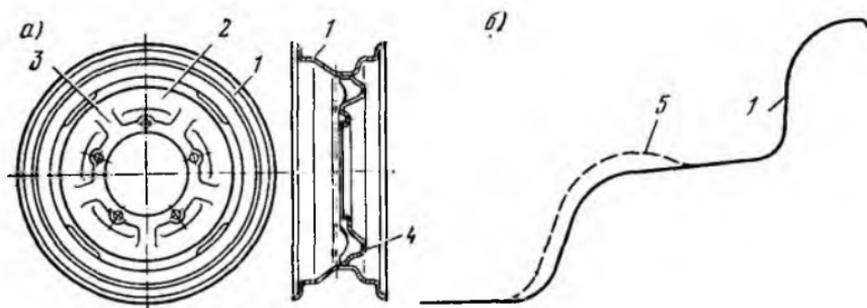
Колесо легкового автомобиля (а) и профиль полки обода (б) для бескамерной шины:
